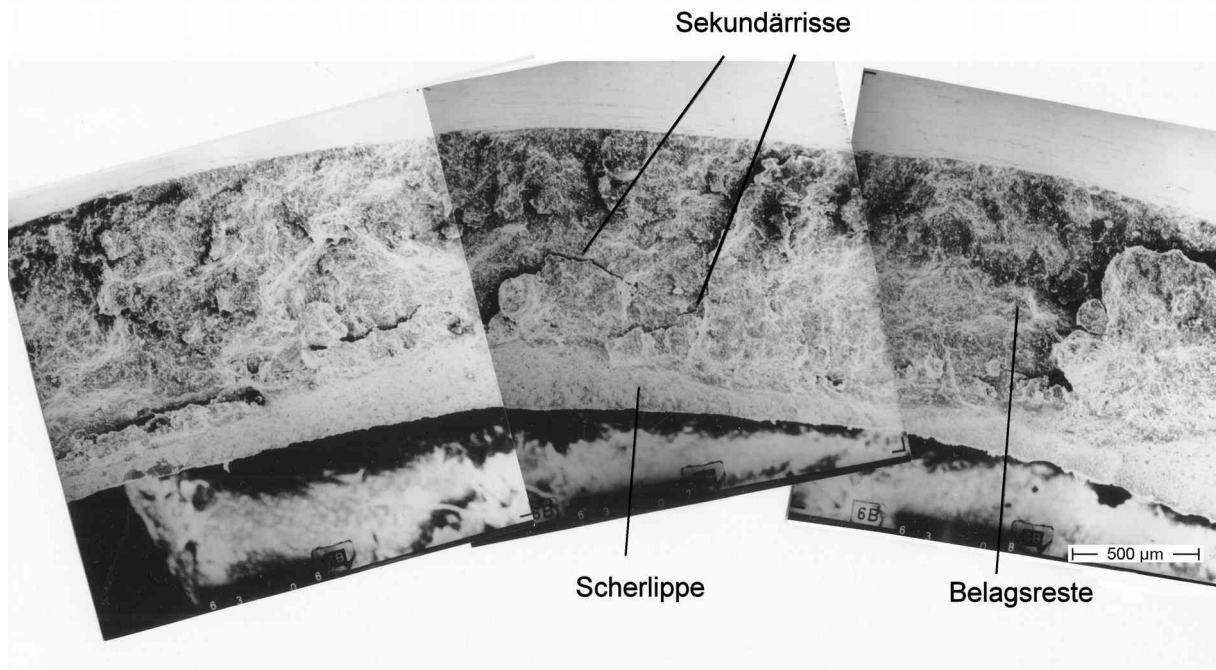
Übersicht mit dem REM; Nebenrisse im Anrissbereich (Ausschnitt aus Bild 1, rechts)
